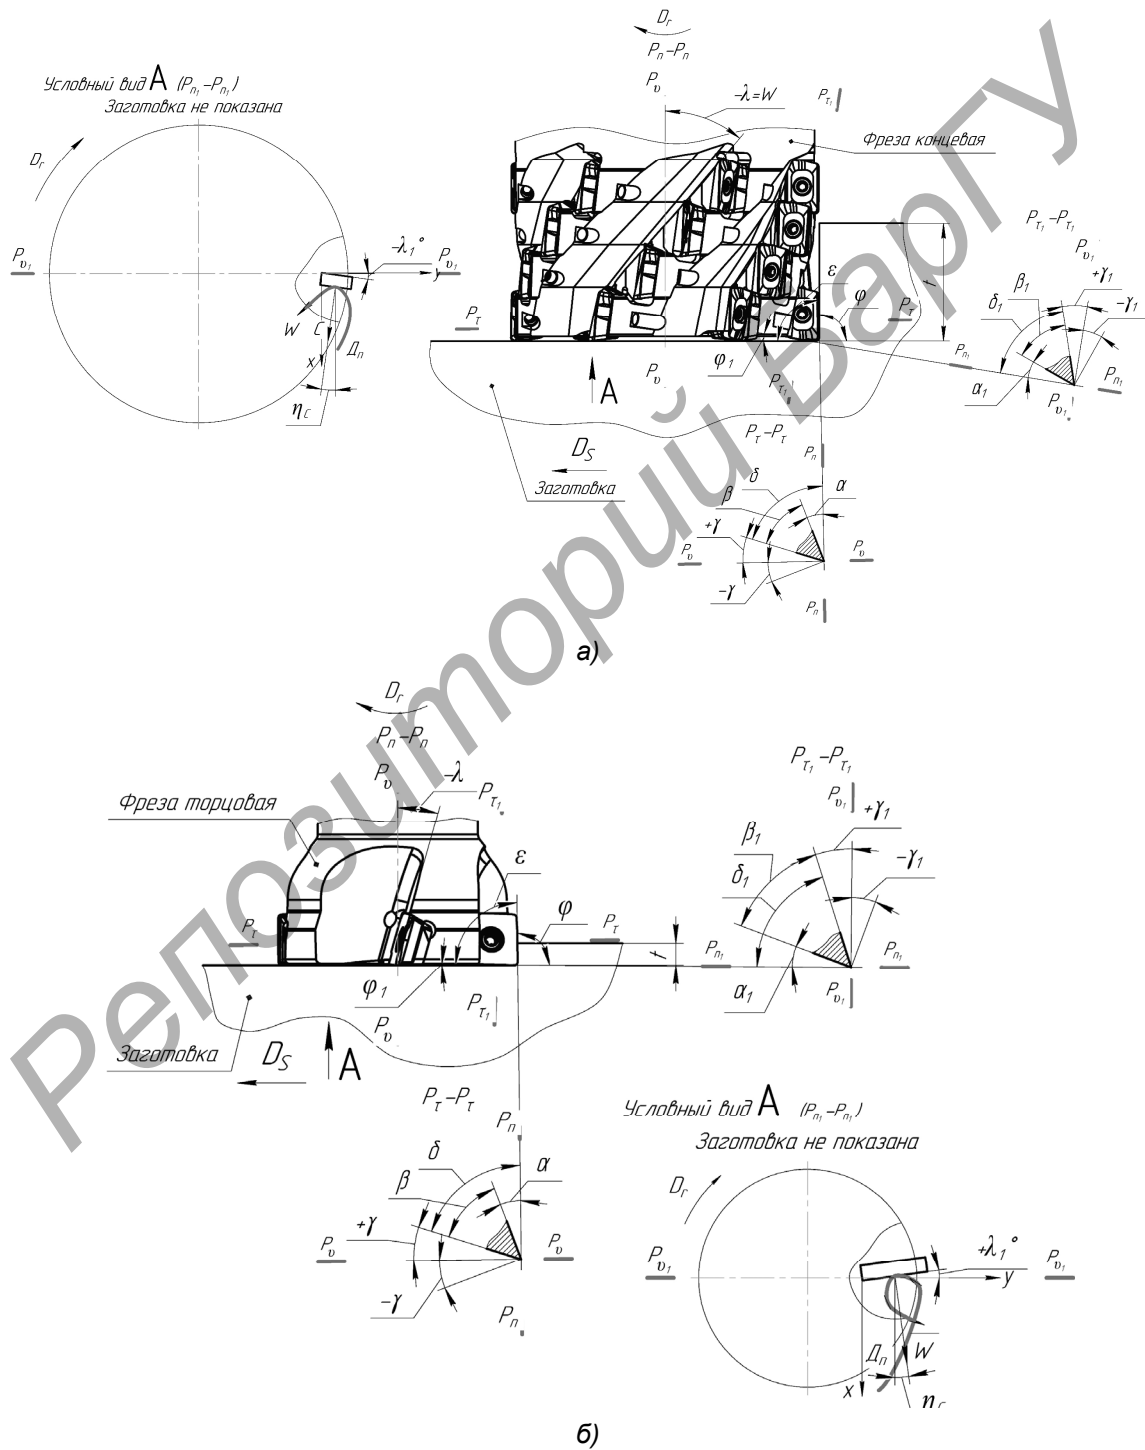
Схемы обработки и геометрические параметры лезвий концевой (а) и торцевой (б) фрез
